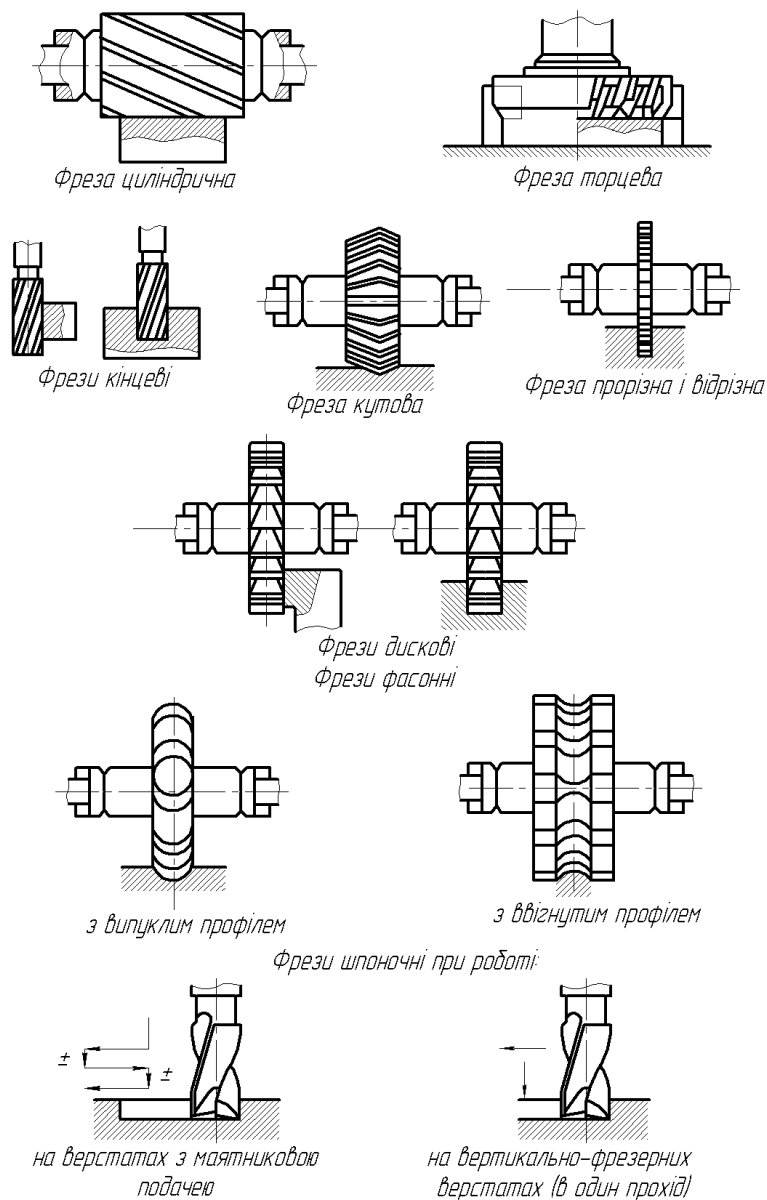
Види фрез і поверхні, які обробляються ними
